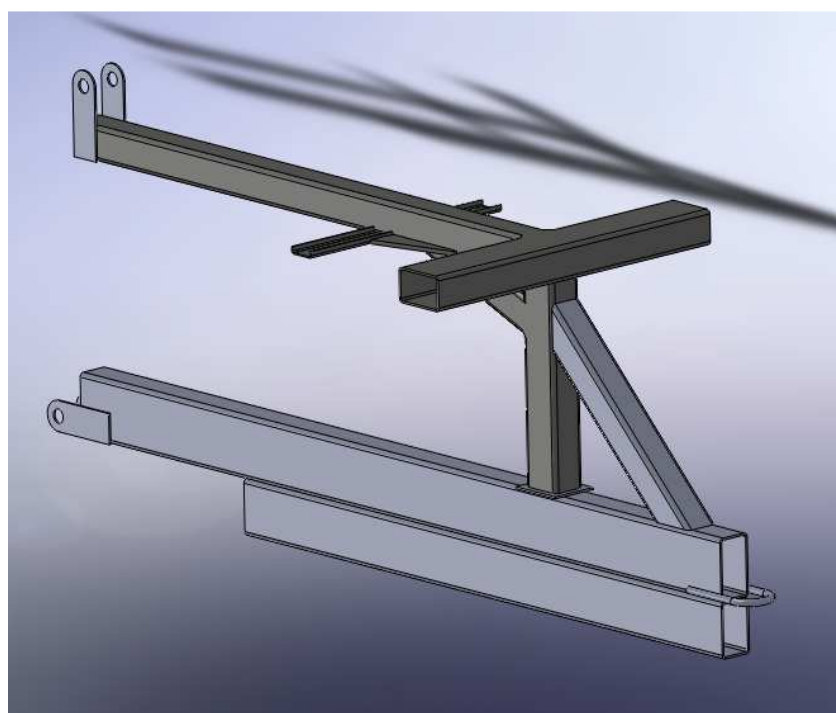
Estrutura de apoio ao ensaio de abertura da ligação pilar estrado
